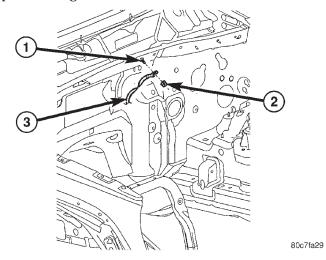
TIRA DE MASA A MOTOR - 2.4L
